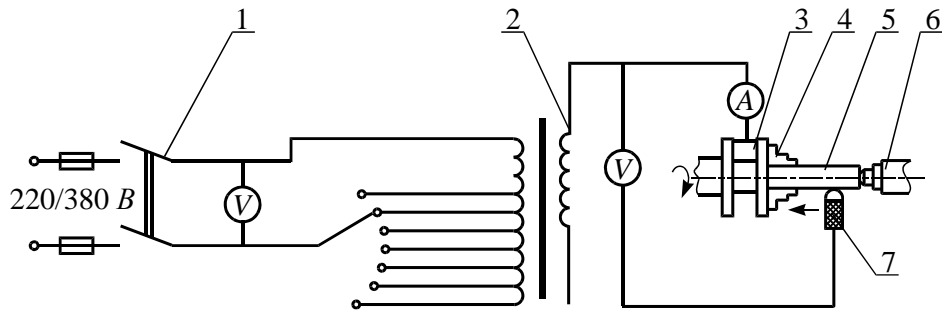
Схема електромеханічної обробки деталі: 1 – вимикач ; 2 – вторинна обмотка; 3 – пристрій для підведення струму; 4 – патрон токарного верстату; 5 – деталь, яка підлягає відновленню; 6 – задня бабка; 7 – пристрій (накатник)
